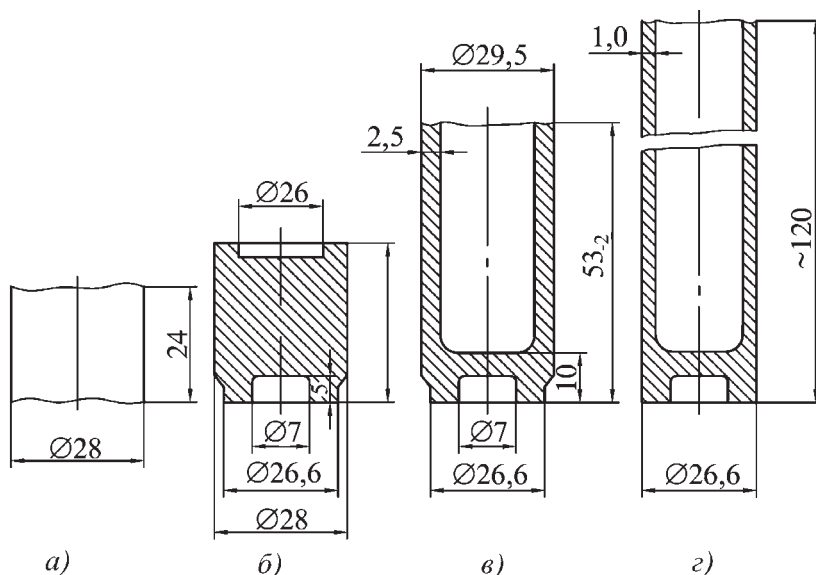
Прессовые операции технологического процесса изготовления детали «корпус» с применением полугорячей штамповки:
